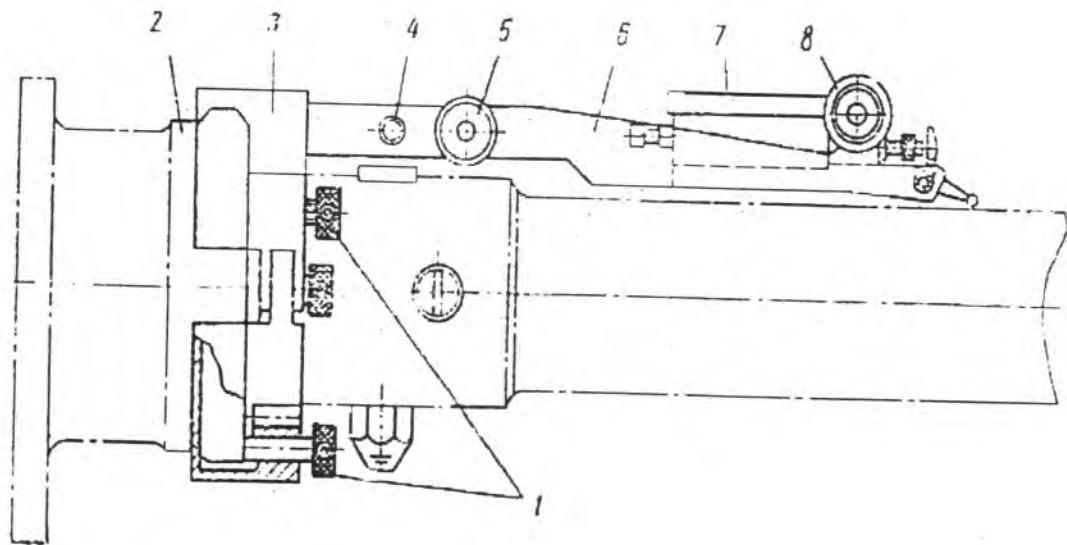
Приспособление 0071-20 для проверки *из люфта* хвостового вала:
